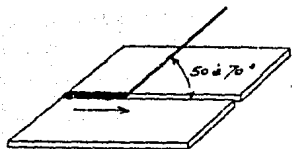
Posición del electrodo en la soldadura horizontal.
